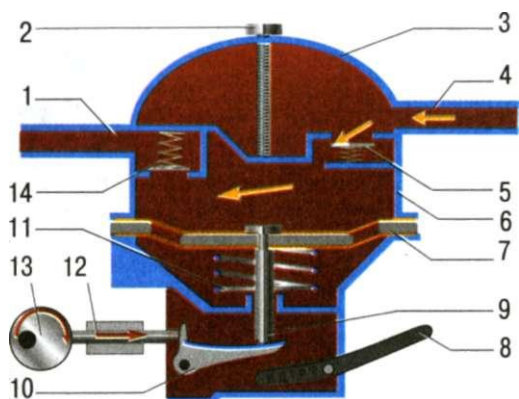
Схема работы топливного насоса (момент всасывания топлива): 1 - нагнетательный патрубок; 2 - стяжной болт; 3 - крышка; 4 - всасывающий патрубок; 5 - впускной клапан с пружиной; 6 - корпус; 7 - диафрагма насоса; 8 - рычаг ручной подкачки; 9 - тяга; 10 - рычаг механической подкачки; 11 - пружина; 12 - шток; 13 - эксцентрик; 14 - нагнетательный клапан с пружиной
